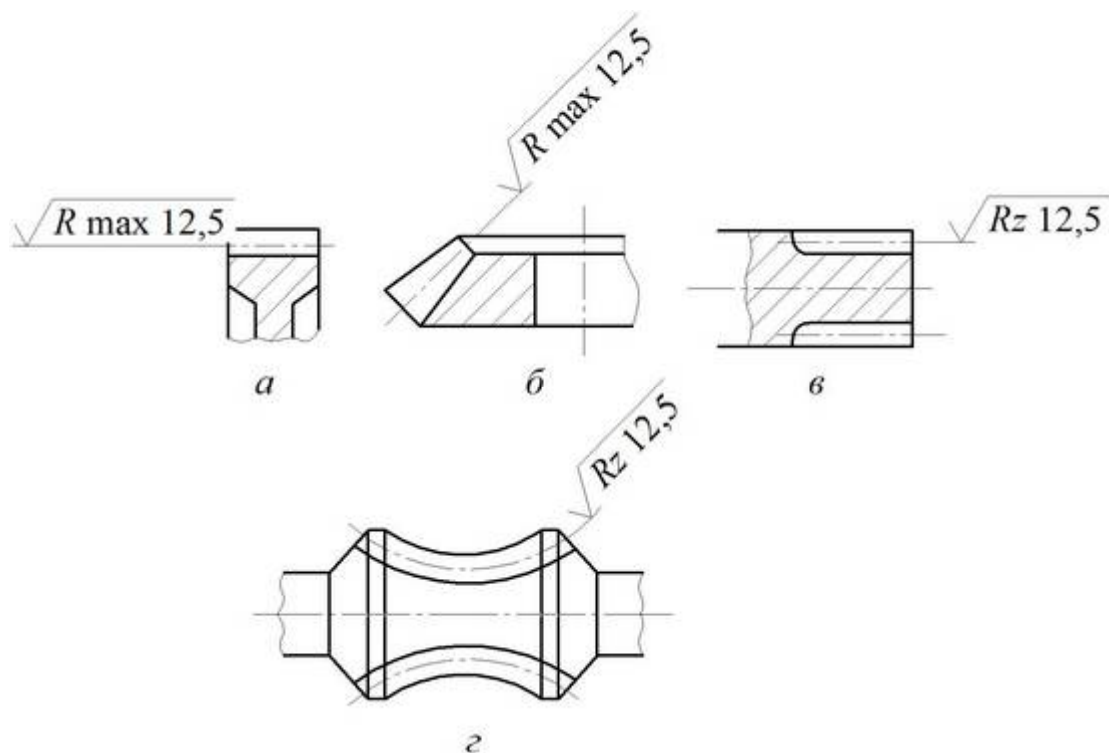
Схема обозначения шероховатости поверхностей зубчатых профилей
